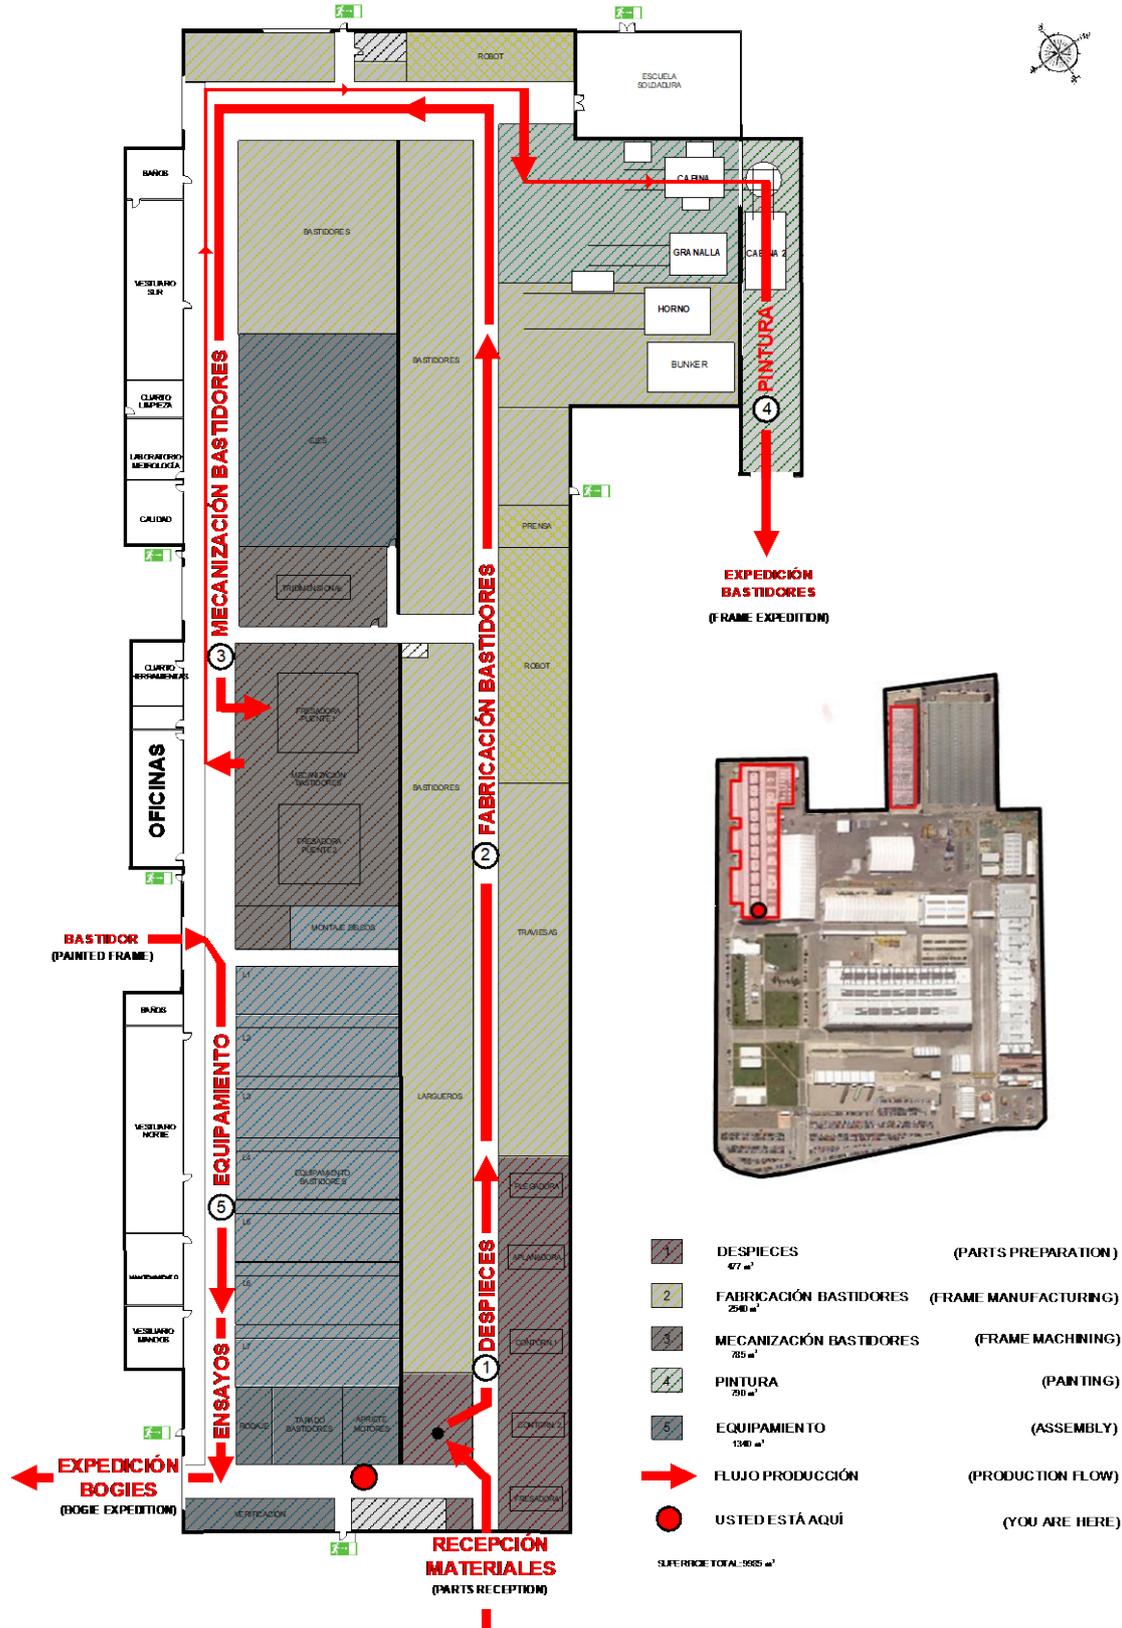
Distribución en Planta del Taller de Bogies. [Fuente: Stadler Rail S.A.U.]
